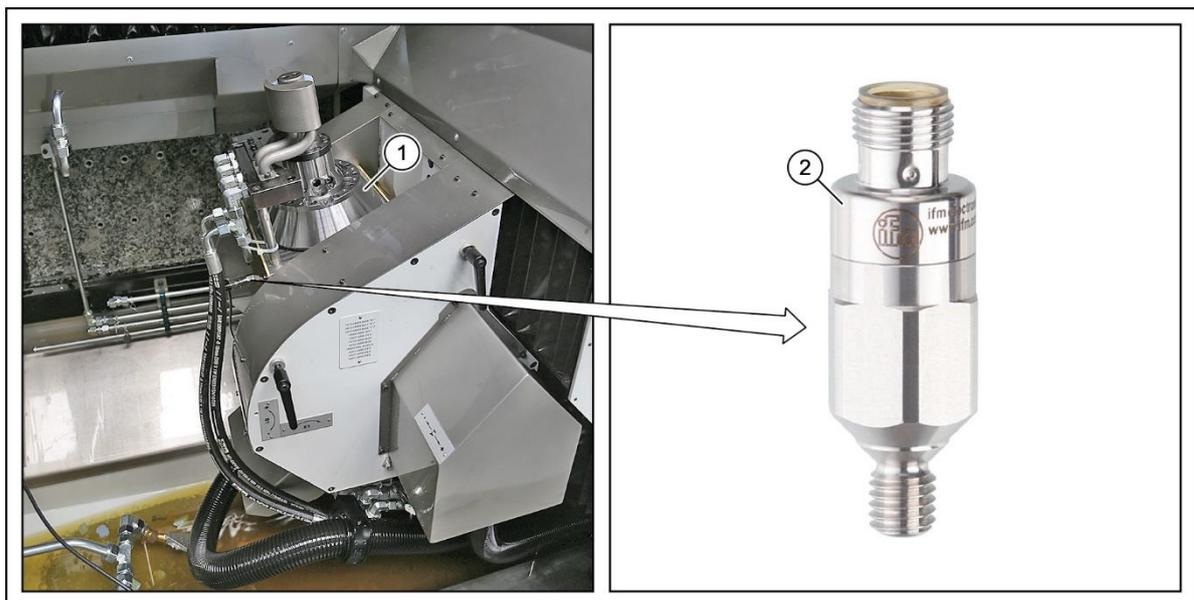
Einachsiger Schwingungssensor an den Werkzeugspindeln - SynchroForm
